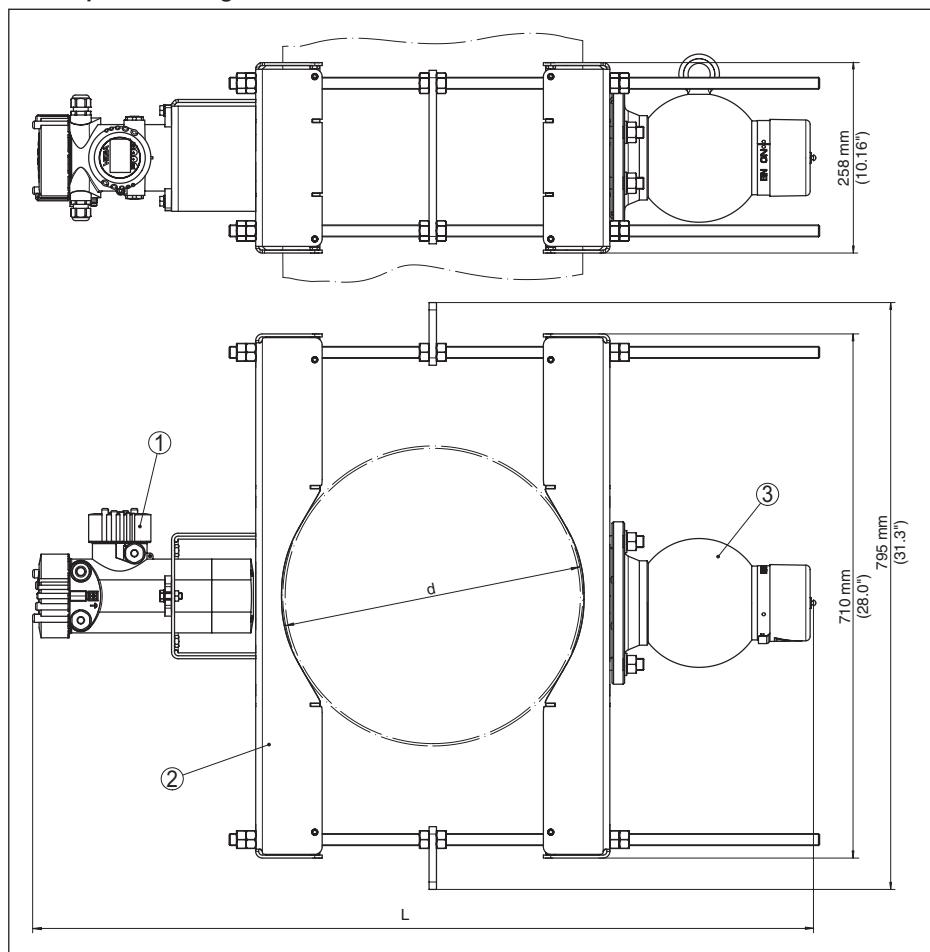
Dispositivo de fixação com sensor montado na posição horizontal
